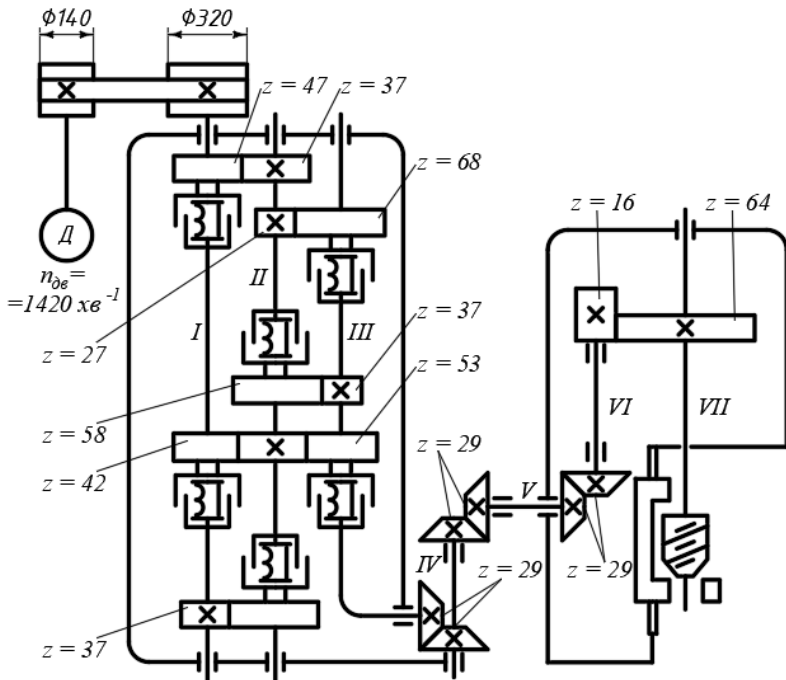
Кінематична схема коробки швидкостей зубофрезерного верстата (приклад)
